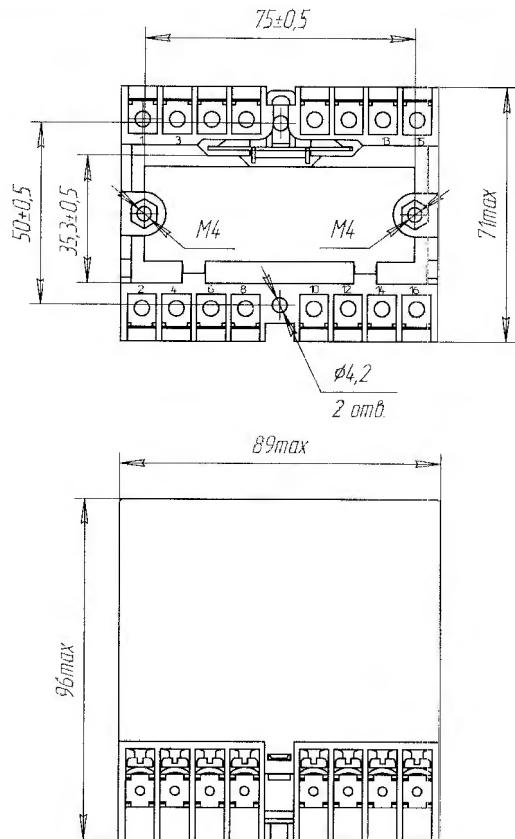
Габаритные, установочные и присоединительные размеры реле РП 18М.
